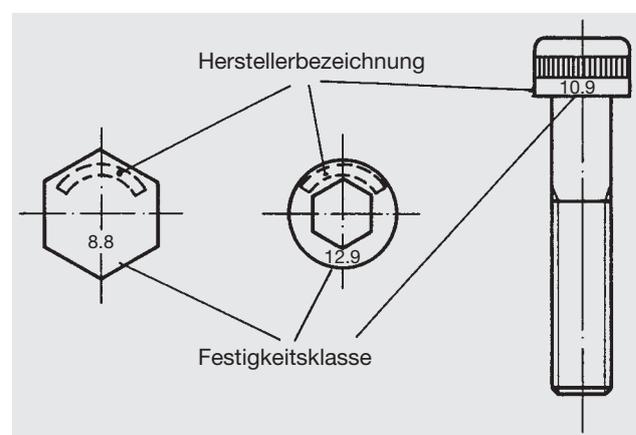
Bezeichnung von Sechskantschrauben und Schrauben mit Innensechskant nach DIN 6914 bzw. DIN 6912.
